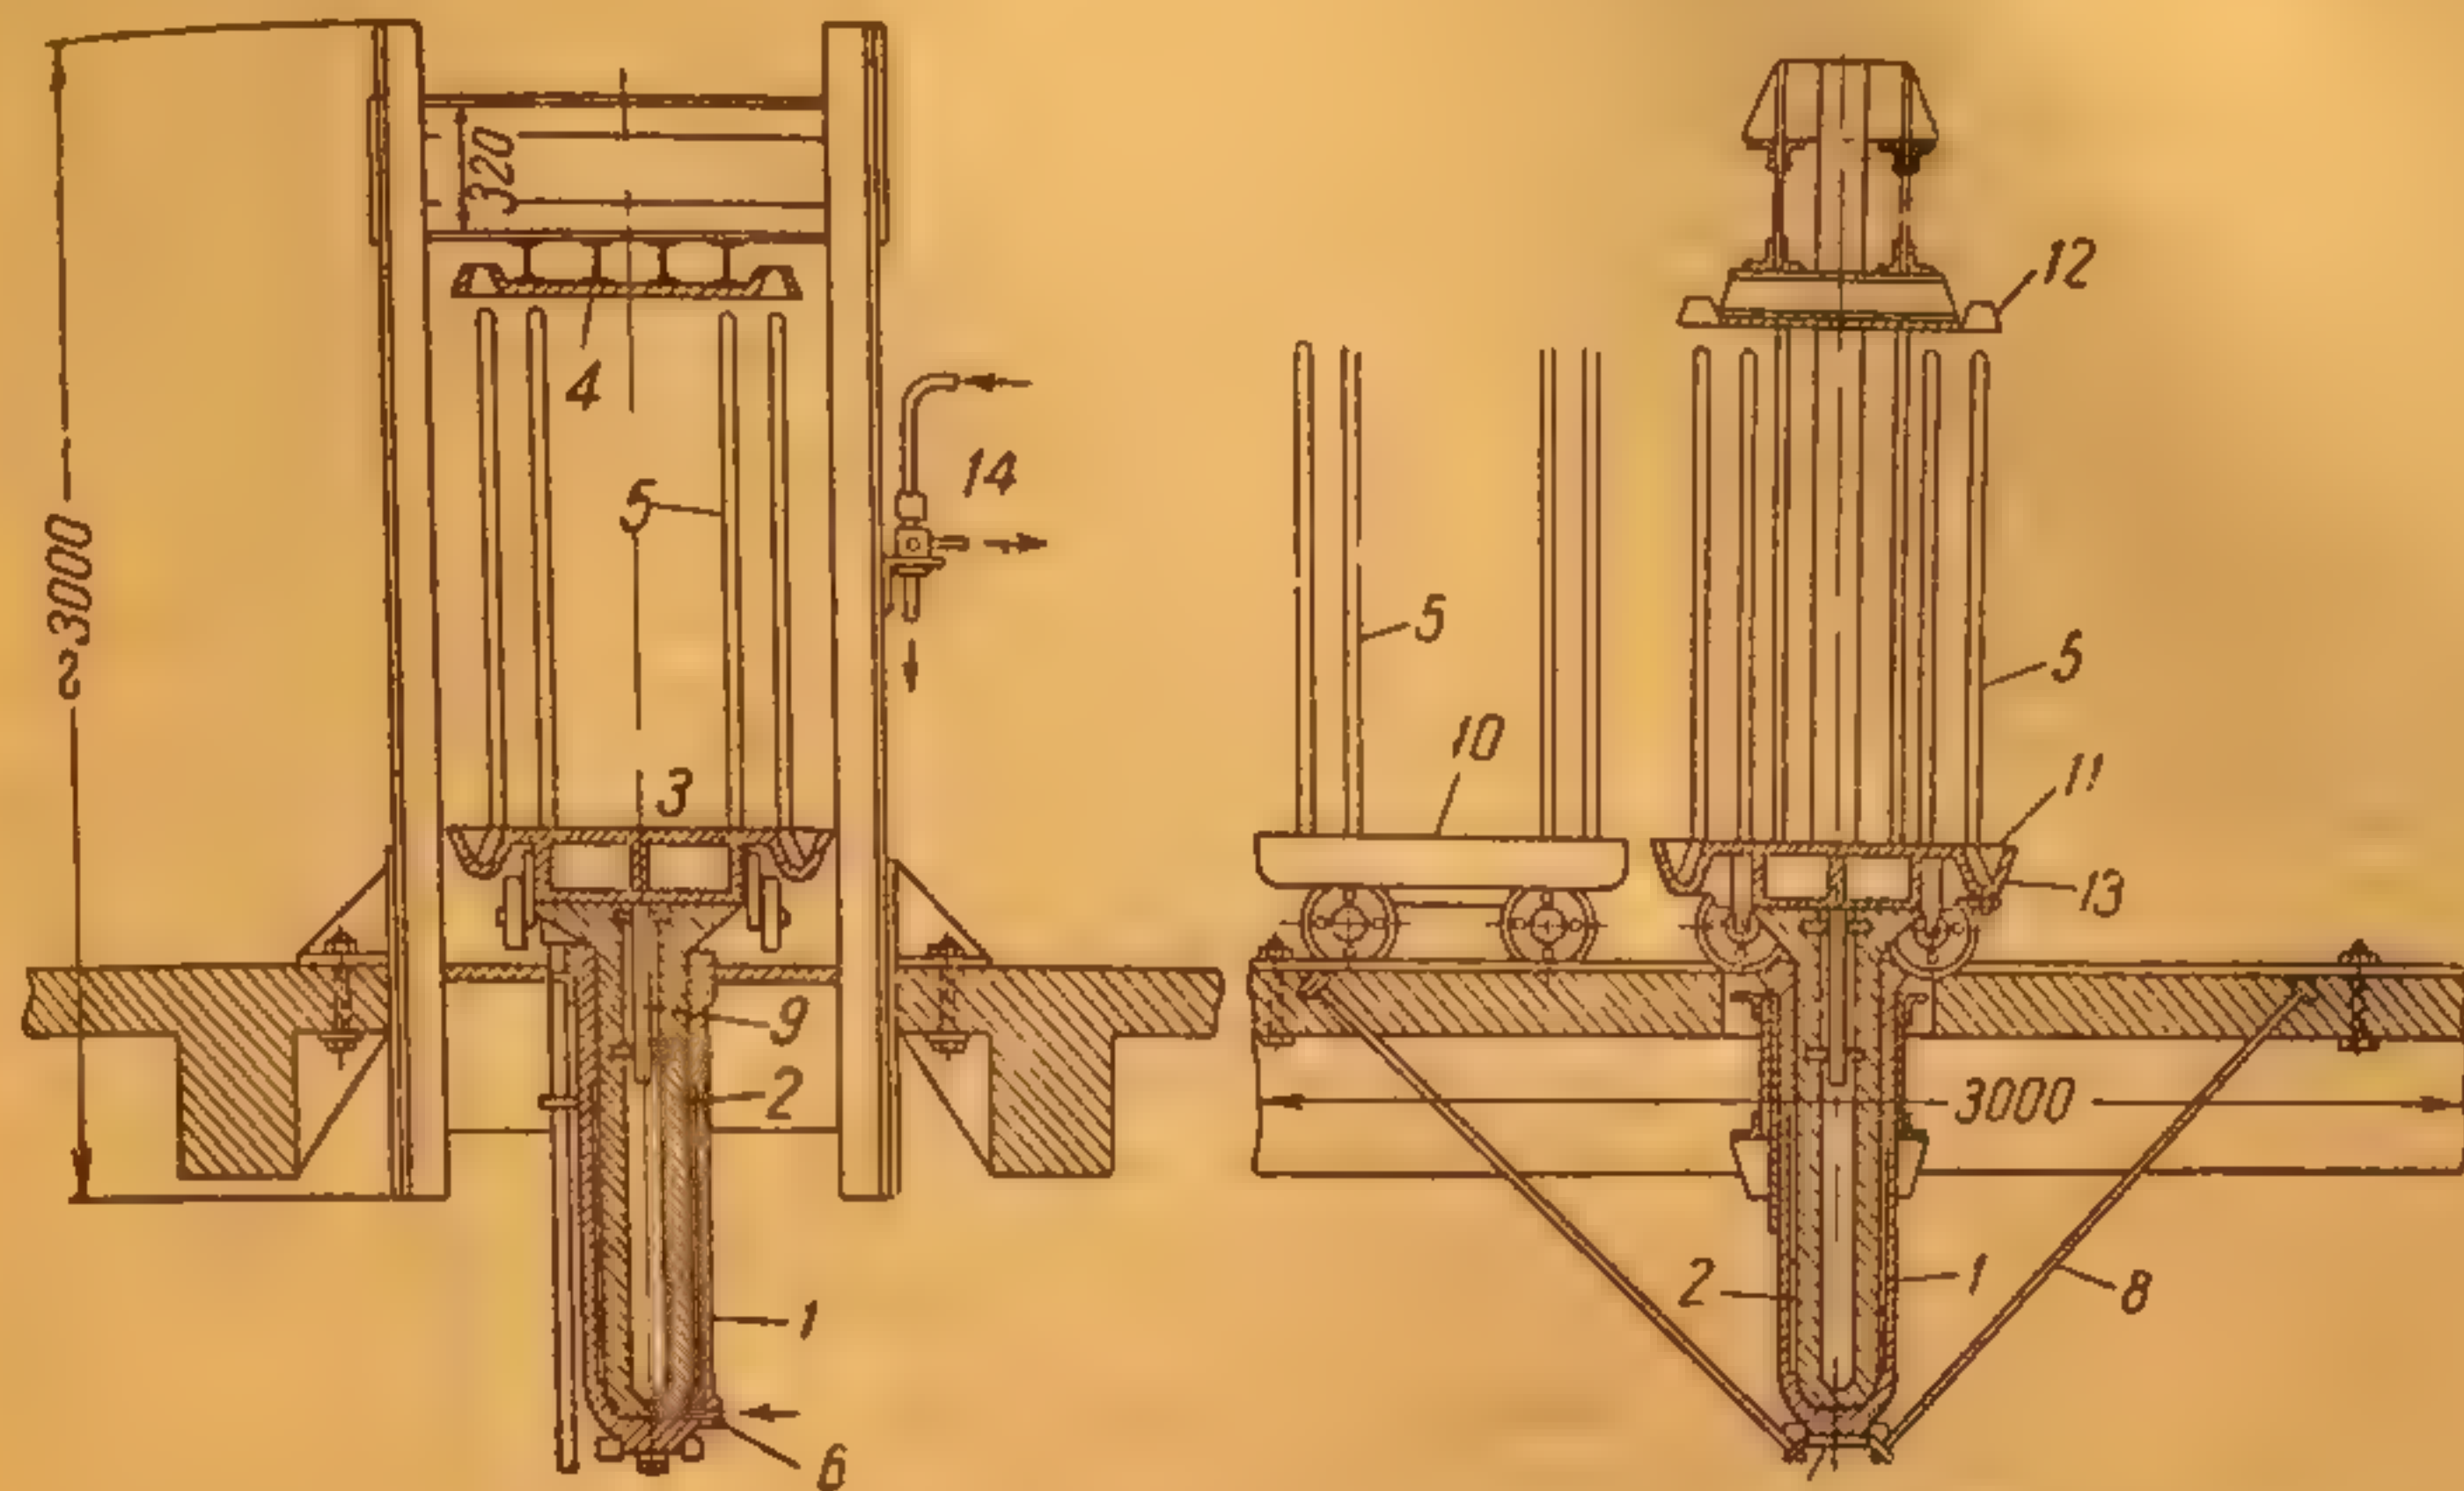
Гидравлический пресс открытого типа с двумя тележками. 1—цилиндр, 2—поршень, 3—подвижная и 4—неподвижная плиты, 5—стойки, 6—труба для подачи масла, 7—хомут, 8—тяги, 9—манжета, 10—корпус тележки, 11—желобки для стока олео, 12—отверстия приливов плиты, 13—отверстия для слива жира, 14—распределительный механизм.
